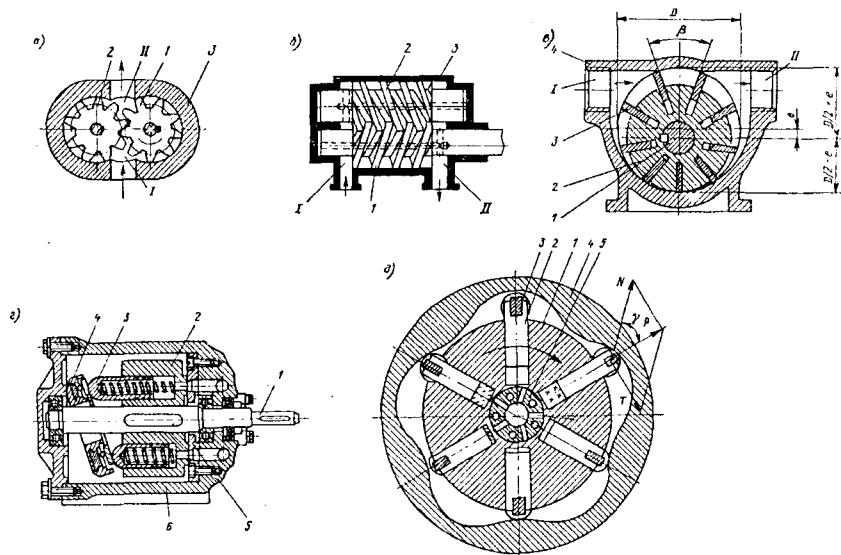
Конструктивные схемы насосов и гидромоторов:
